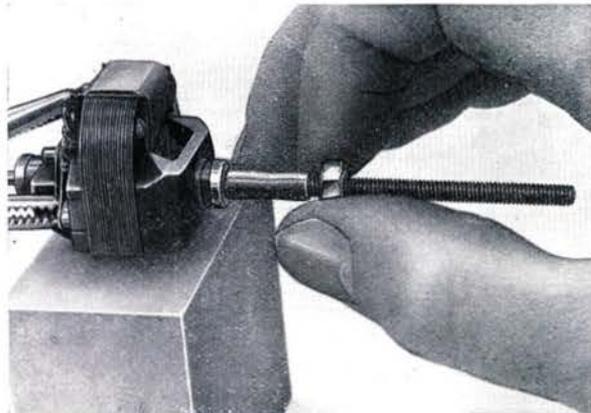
Motor mit Gewindebolzen zum Zählen der Umdrehungen
